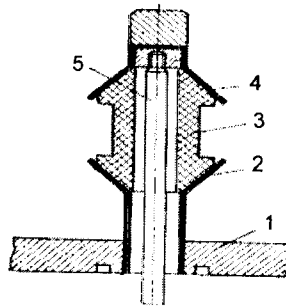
Високовольтний керамічний струміввід для надвисоковакуумних систем: 1 – корпус; 2, 4 – металеві ковпачки; 3 – керамічний ізолятор; 5 – струмопровідний стрижень
